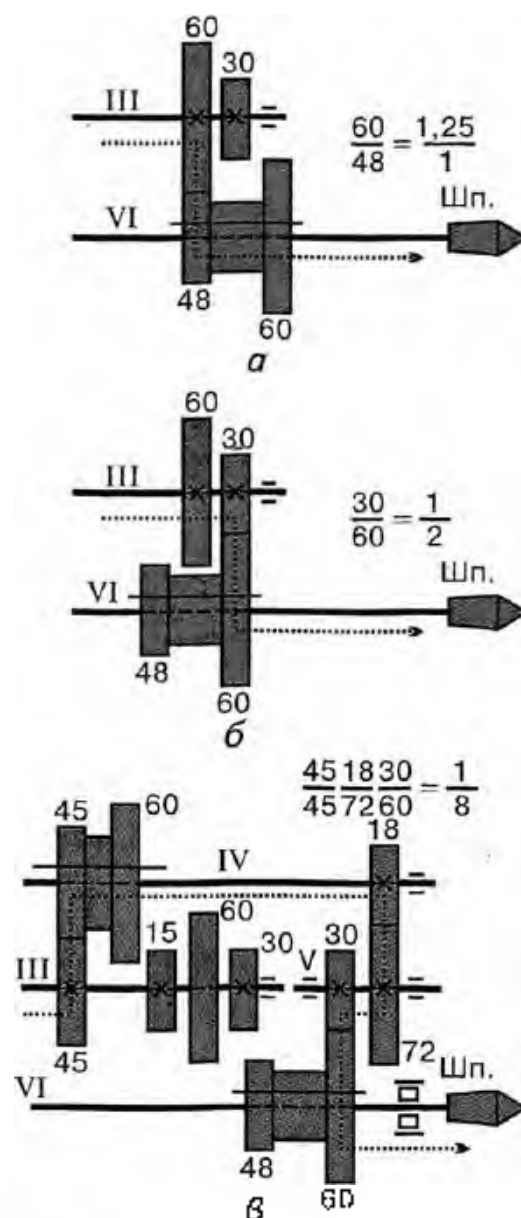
СХЕМА ПЕРЕДАЧІ ОБЕРТАННЯ З ВАЛА III НА ШПИНДЕЛЬ (ВЕРСТАТ 16К20)
